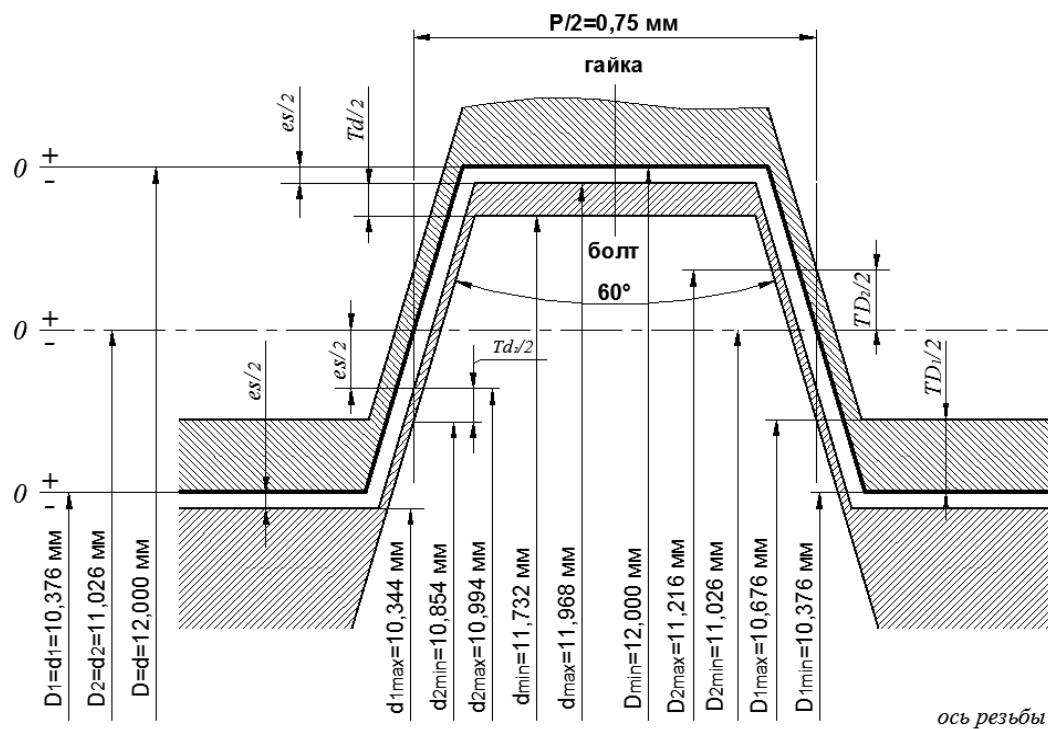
Схема расположения полей допусков резьбового соединения $M12 \times 1,5-6H/6g$
